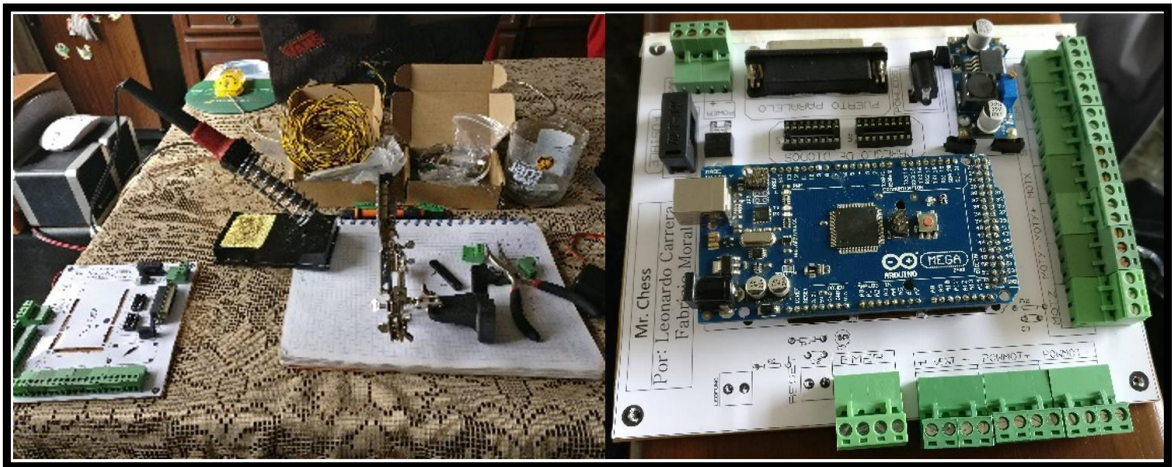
De izquierda a derecha: suelda de elementos, placa terminada.
